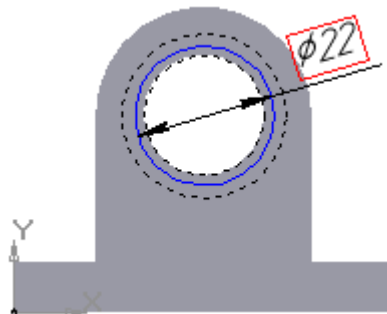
Побудова ескізу заглиблень під підшипники
